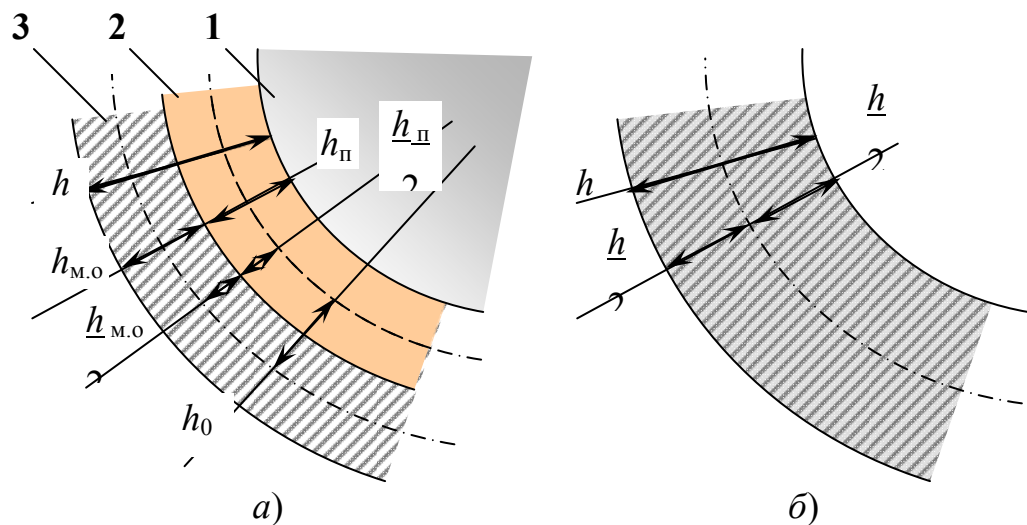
Расчётные толщины корпуса сферического подшипника скольжения: а – разрез двухслойного корпуса, б – модель эквивалентного однослойного корпуса
